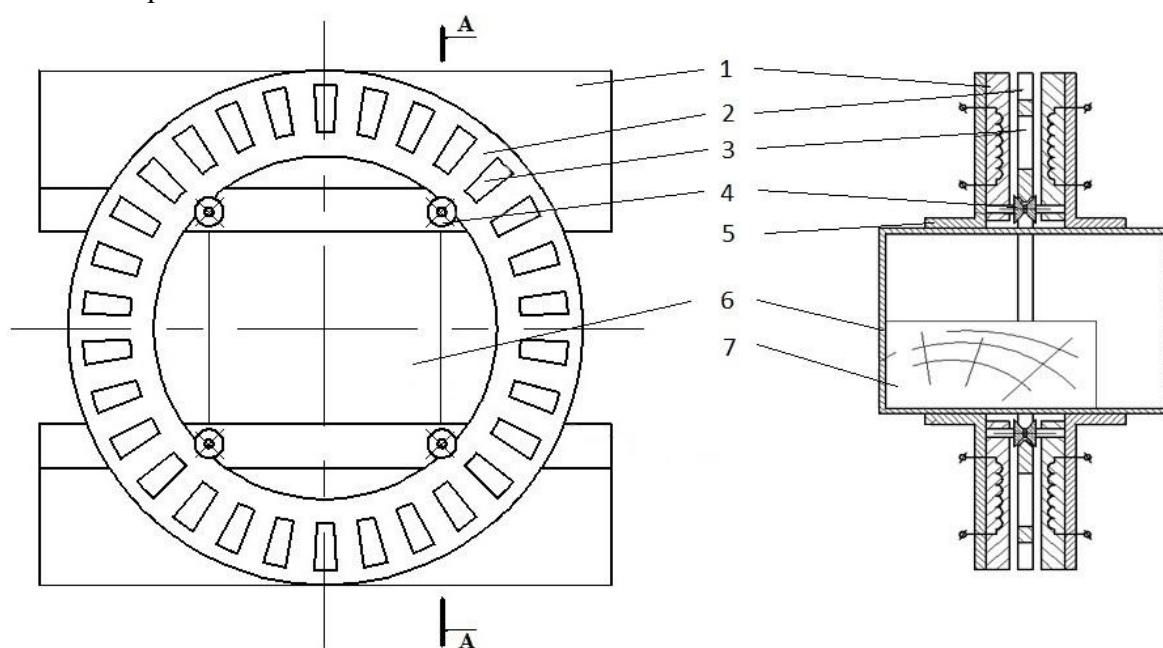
Схема пильного модуля с кольцевой пилой: 1 – статор; 2 – пила-ротор; 3 – постоянный магнит; 4 – опорно-направляющий ролик; 5 – крепление входного отверстия для пиломатериалов; 6 – входное отверстия для пиломатериалов; 7 – заготовка.
